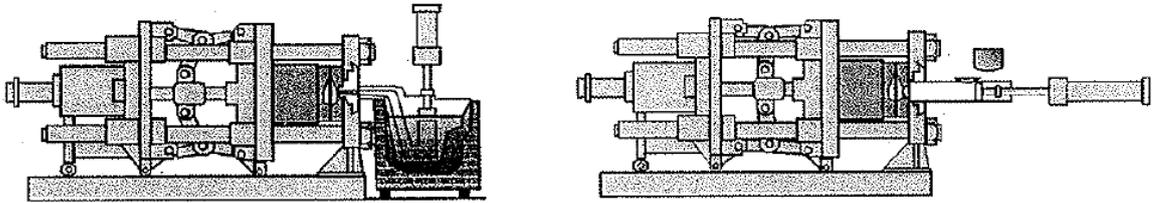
À esquerda, exemplo de uma máquina de fundição injetada em câmara quente. À direita, exemplo de uma máquina de fundição injetada em câmara fria.
